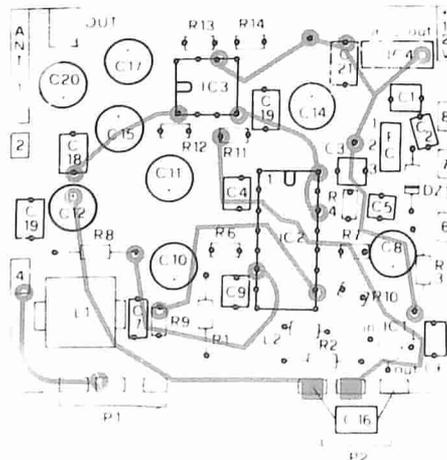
Disposizione delle piste sul lato superiore dello stampato.
